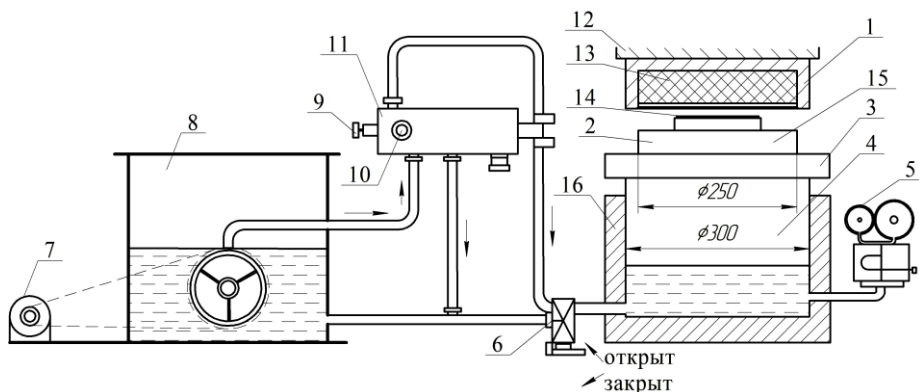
Схема лабораторного пресса для штамповки эластичной средой:
